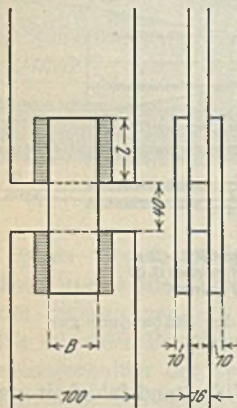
Dauerzugversuche mit Lichtbogenschweißungen, Laschenanschlüsse St 37.
